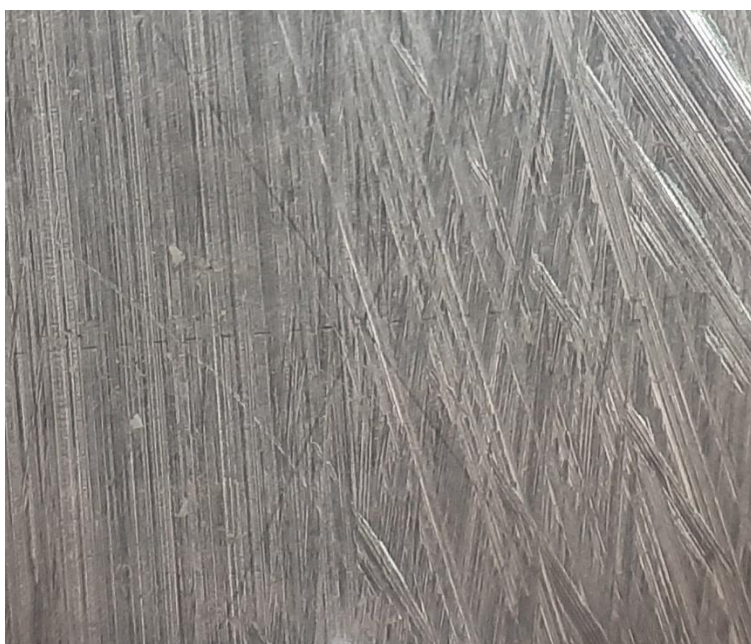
Поверхность титана марки ВТ6ч до сварки
